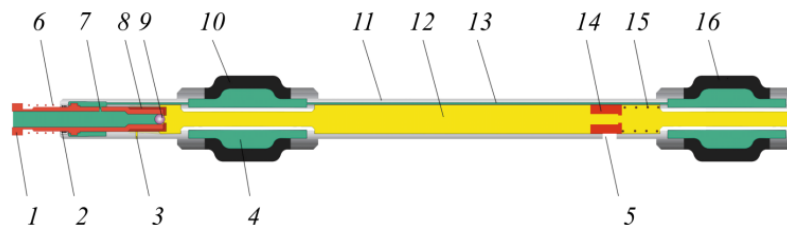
Схема установки многостадийного гидроразрыва пласта: 1 – управляющий механизм байонета «J» в положении для раздувания; 2 – подшипник; 3 – выпускной порт; 4 – наполнитель пакера; 5 – канал выпуска пропанта; 6 – пружина; 7 – порт для раздувания пакеров; 8 – цанговый зажим; 9 – фенольный шар; 10 – пакер 1; 11 – корпус установки; 12 – рабочее пространство установки; 13 – капилляр, соединяющий пакеры; 14 – многоцелевой клапан; 15 – пружина; 16 – пакер 2
